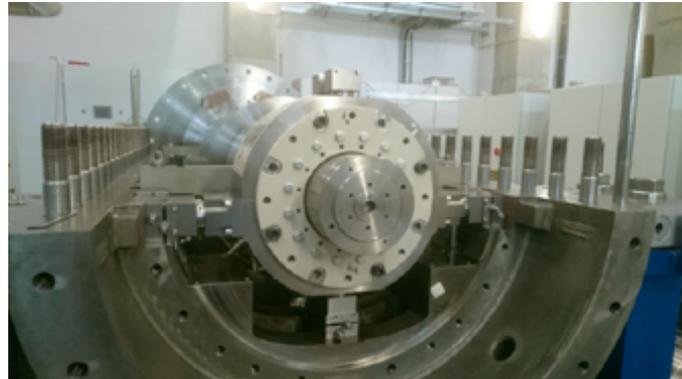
Sensorstator zur kombinierten Messung der axialen und radialen Rotorlage
